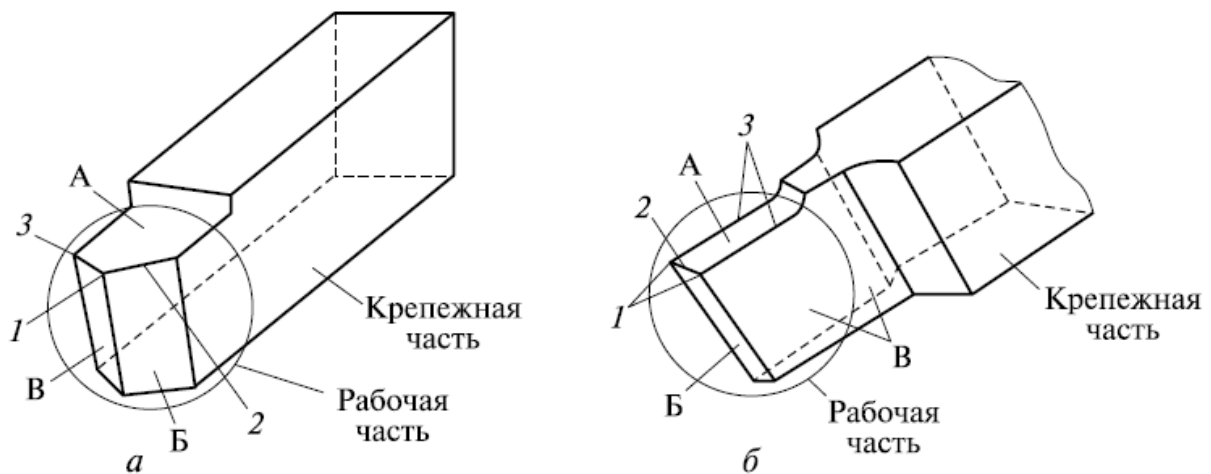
Элементы рабочей части проходного (а) и отрезного (б) резца: 1 — вершина резца; 2 — главная режущая кромка; 3 — вспомогательная режущая кромка; А — передняя поверхность; Б — главная задняя поверхность; В — вспомогательная задняя поверхность
